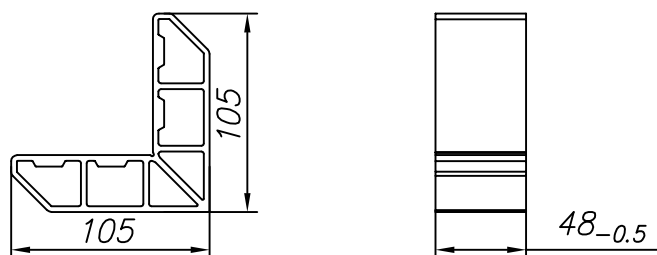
Изготовление соединителя углового FLGU.400.0910
